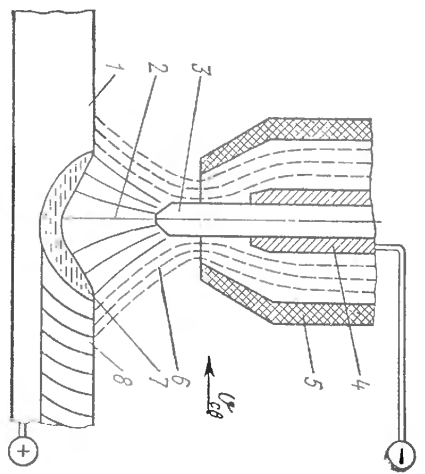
Схема дуговой сварки в защитном газе:
